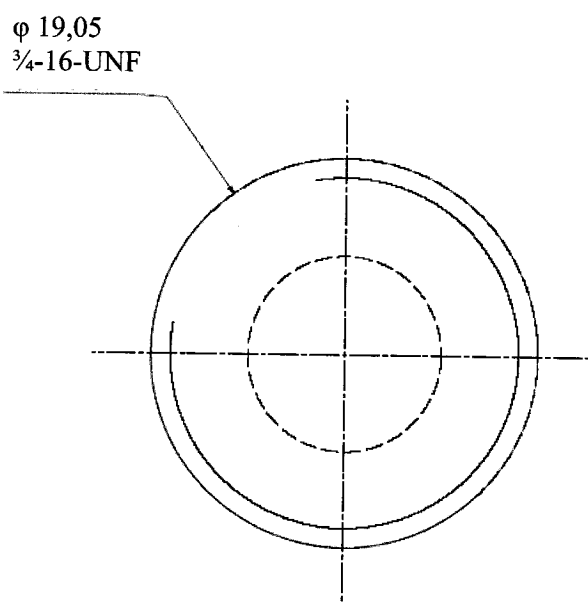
Dimensions de l'éprouvette avec canal utilisée pour la calibration du procédé, exprimées en millimètres
